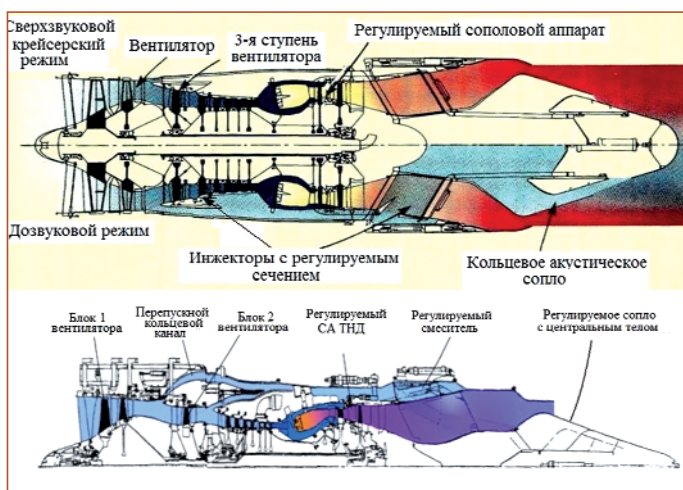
Варианты конструктивной схемы двигателя XF120
